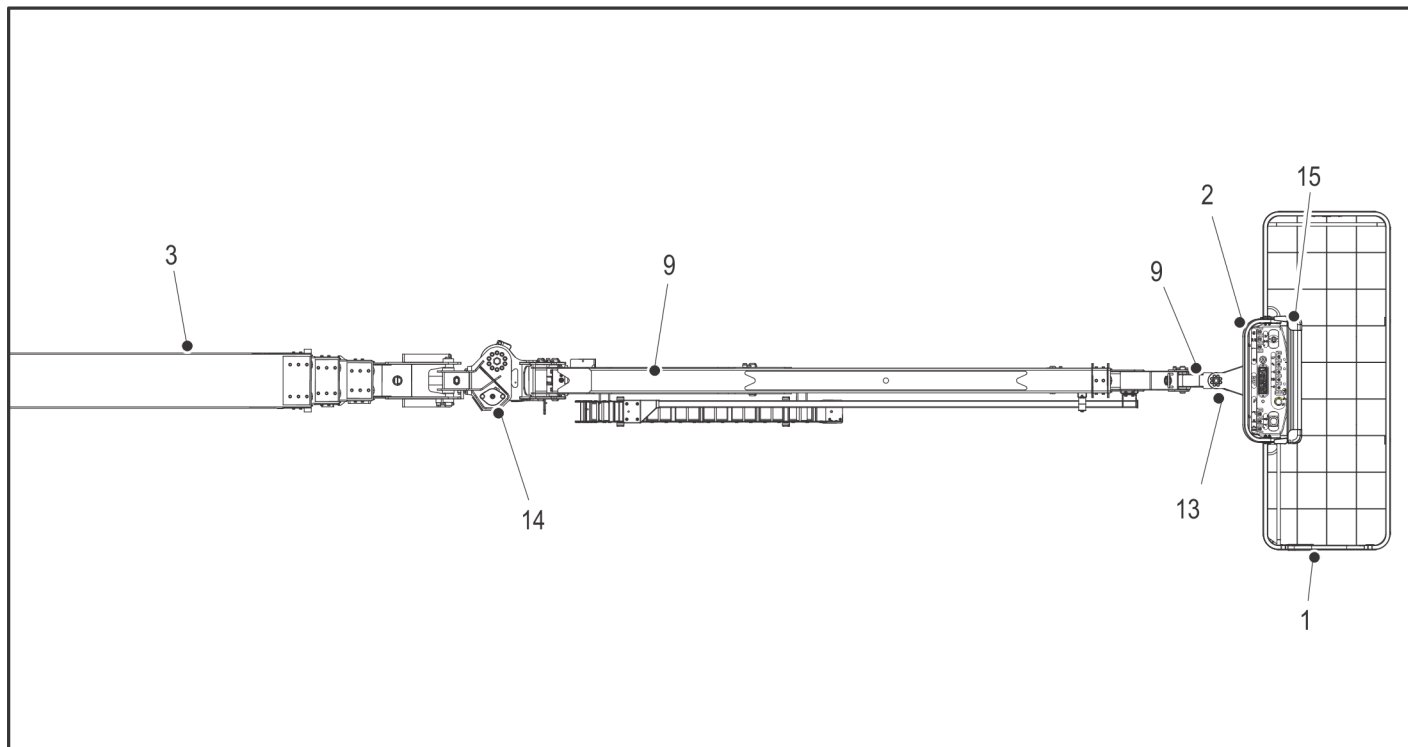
Grundlæggende komponenter – Blad 1 af 3
